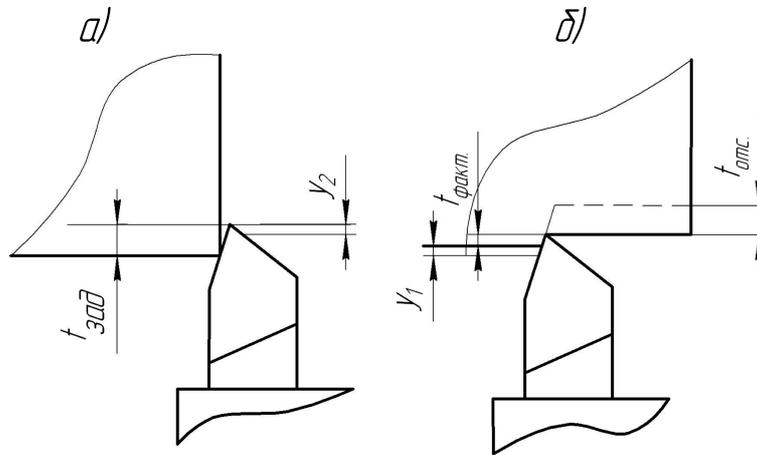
Схема к определению упругих отжатий инструмента (а) и заготовки (б)
